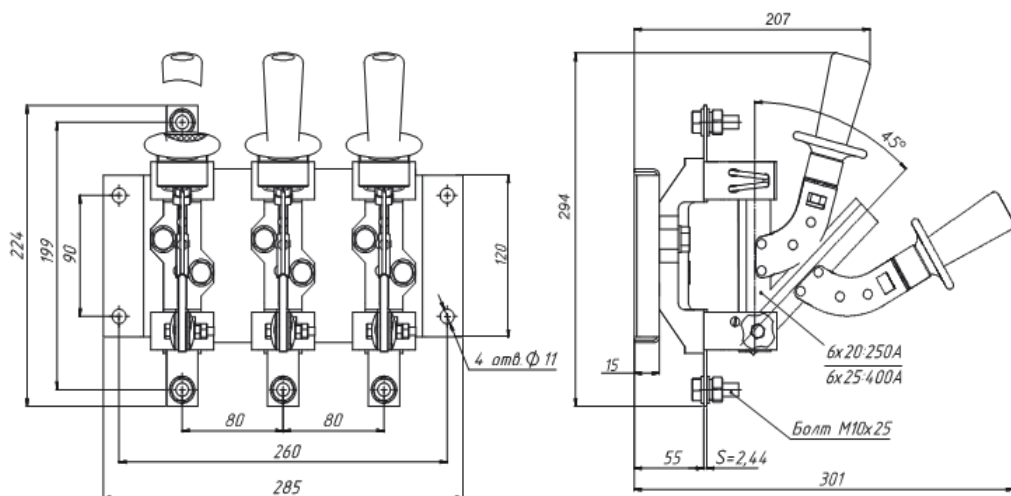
Разъединитель РЕ19-35(37)-31160-00 УХЛ3 с рычагом для полюсного оперирования штангой
